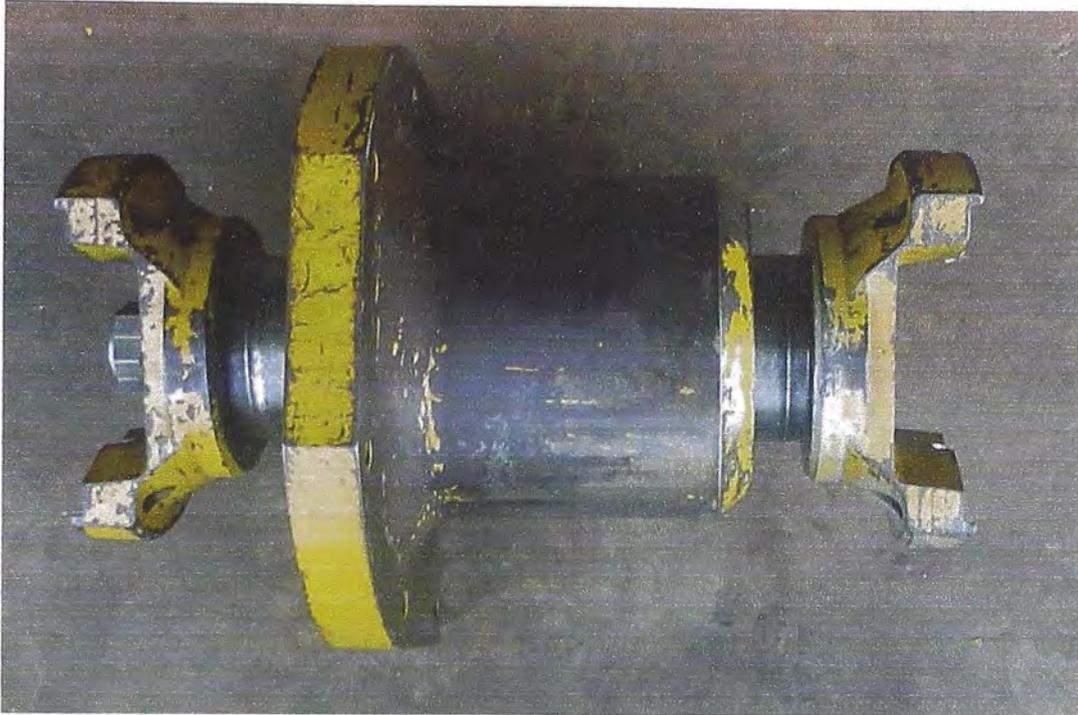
caja de rodamientos de línea cardánica modificada.
